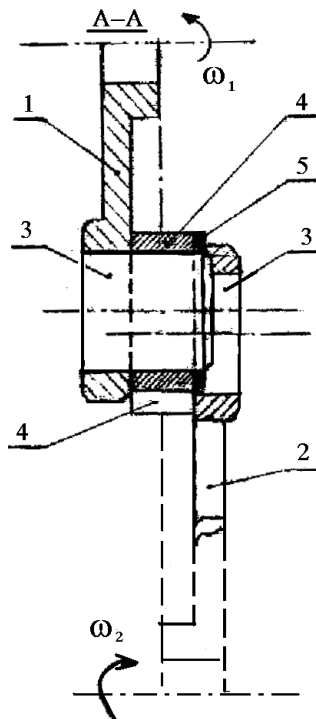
Схема передачи вращательного движения с относительно подвижными цилиндрическими элементами зацепления
